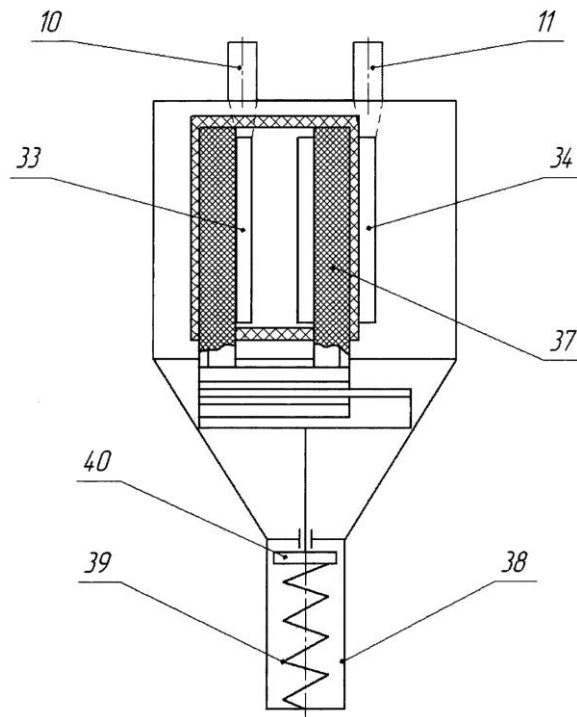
Привід вкладиша: 10 і 11 - патрубок; 33 і 34 - паз; 37 - вкладиш; 38 - пневмоциліндр; 39 - пружина; 40 - поршень.
